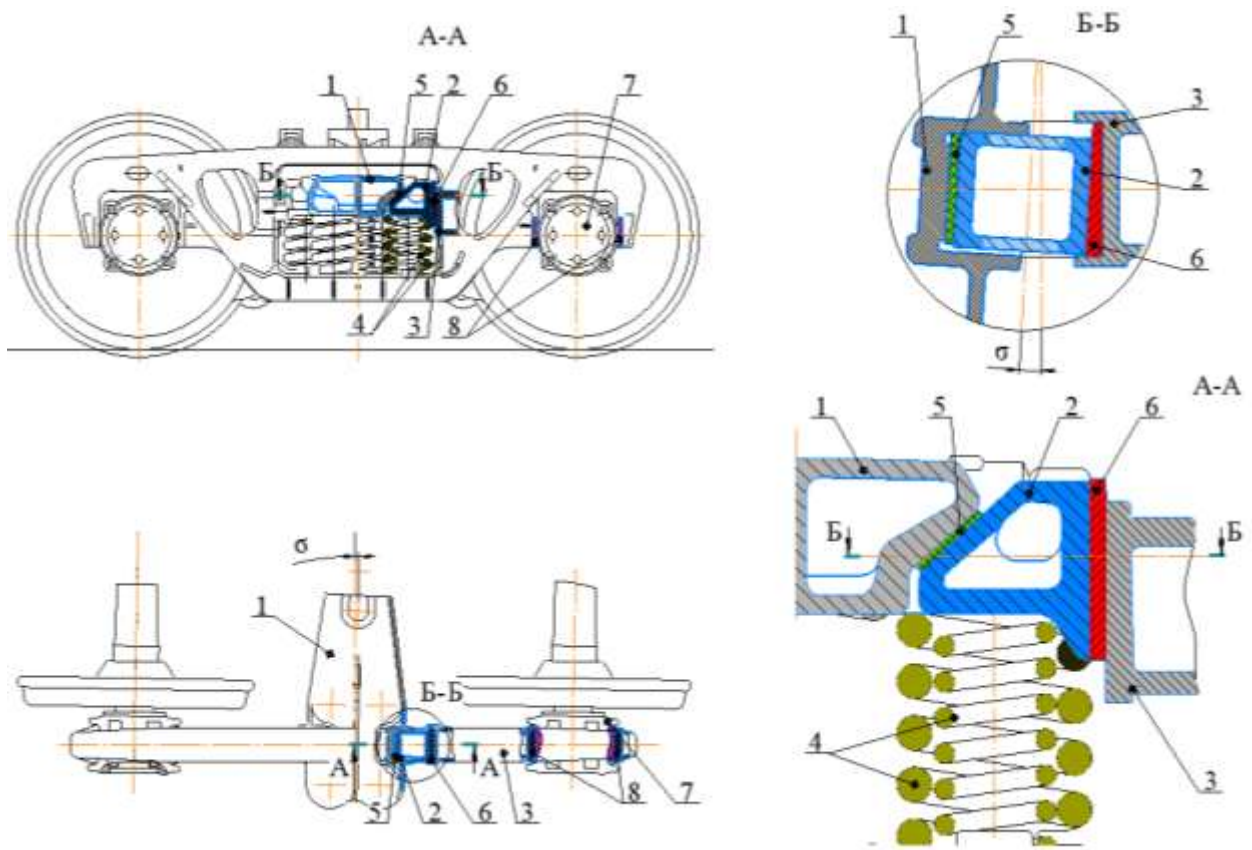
Схема з'єднання шворневої балки через фрикційні клини з боковинами рами
